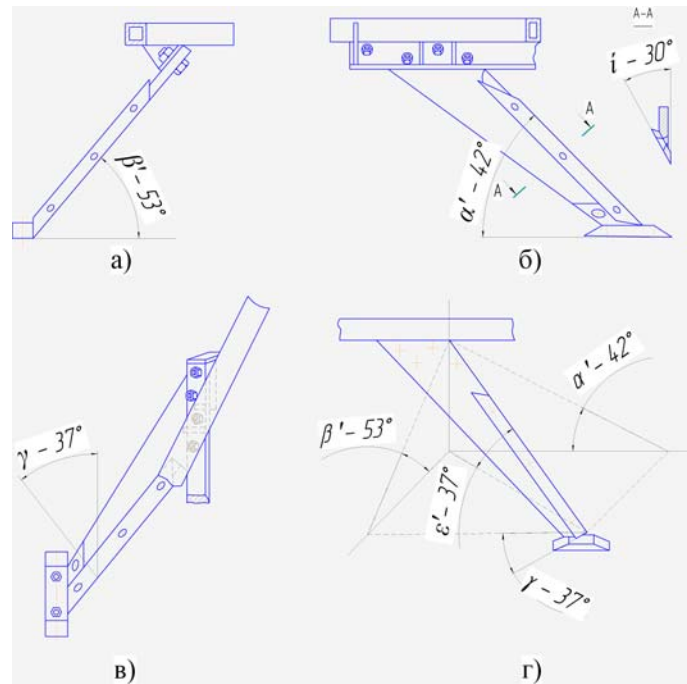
Конструктивні параметри установки робочого органу нахилого розпушувача: а) – вигляд спереду; б) – вигляд збоку; в) – вигляд зверху; г) – аксонометрія
